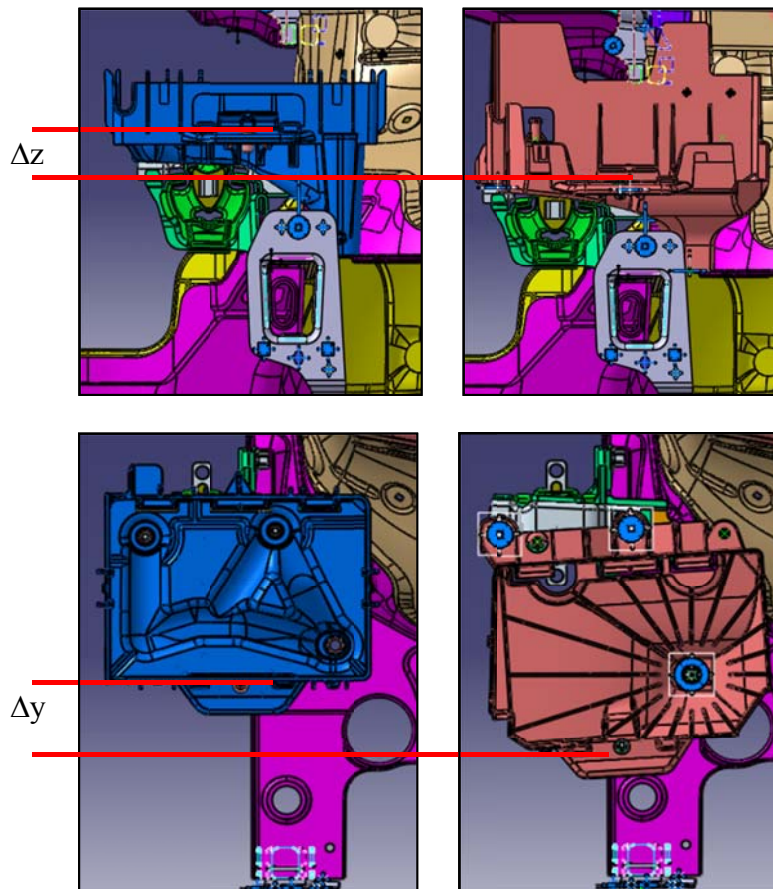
Comparación en alzado y planta de dos tipos de consolas
